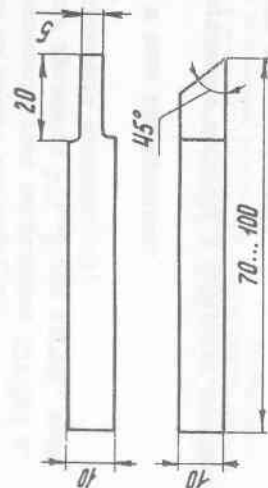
Боек для изготовления искусственных дефектов типа зарубок
